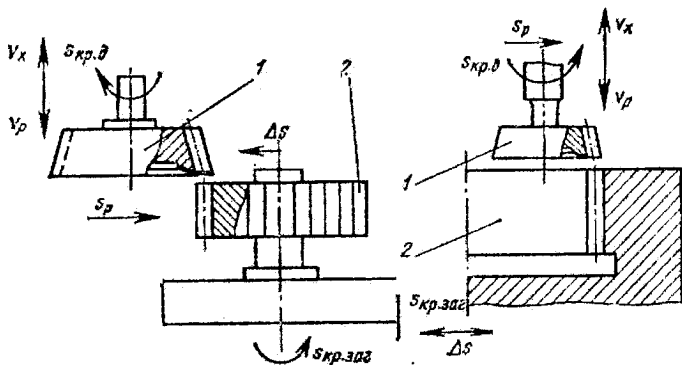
Схема обробки зубчастих коліс довбанням:
